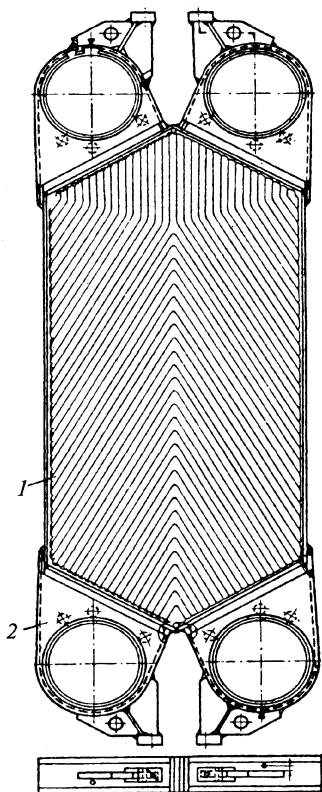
Сварной блок из гофрированных пластин
